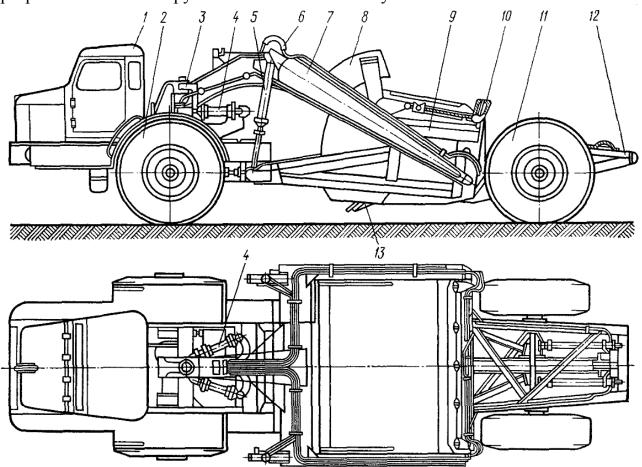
Конструктивная схема полуприцепного скрепера:
